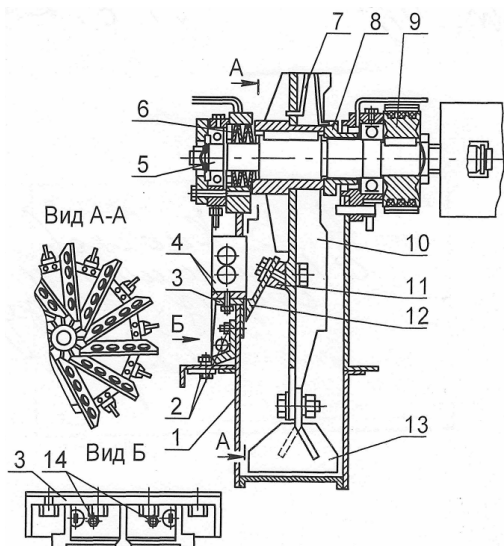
Измельчающий аппарат: 1 – камера; 2 – болты крепления подбрусника; 3 – подбрусник; 4 – противорежущие пластины; 5 – вал; 6 – тарельчатая пружина; 7 – стопорная пружина; 8 – гайка; 9 – шкив; 10 – ротор; 11 – опора; 12 – нож; 13 – лопатка; 14 – регулировочные болты
